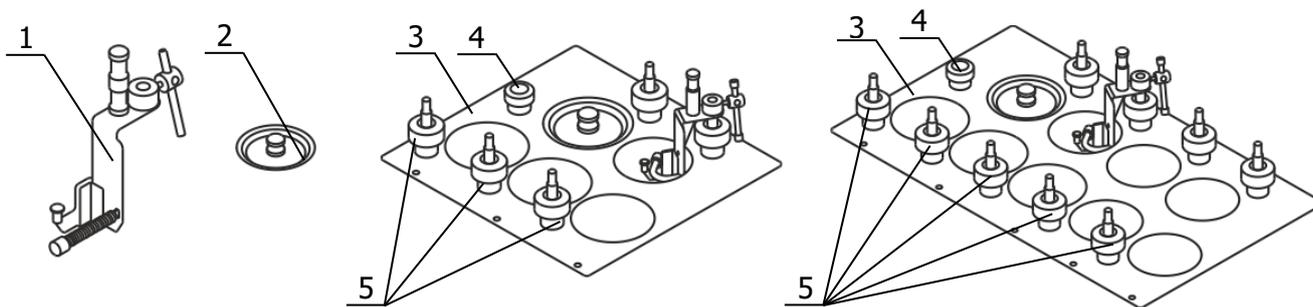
Внешний вид комплектов приспособлений ВИС-Т-06-5К и ВИС-Т-06-9К
